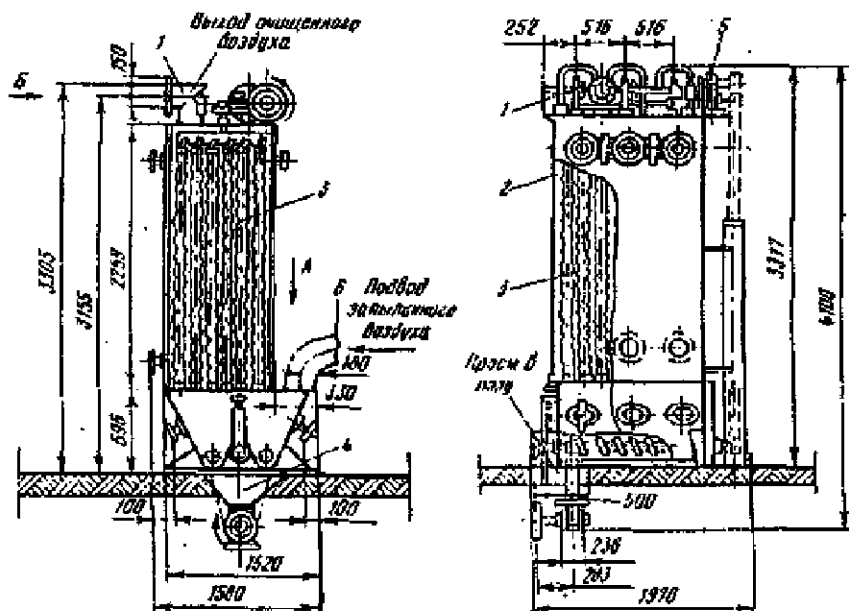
Рукавный фильтр всасывающий типа ФВ (Г4-1БФМ): 1 - клапанные коробки для выхода воздуха; 2 - шкаф металлический; 3 - рукава; 4 - сборник пыли; 5 - электродвигатель; 6 - входной патрубок.
